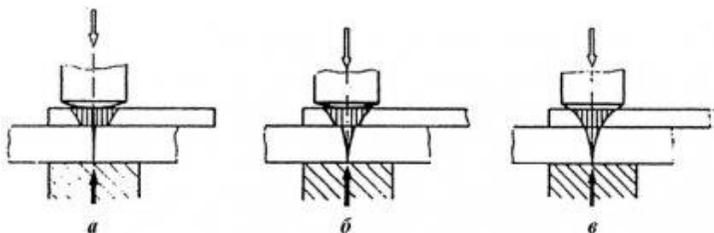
Распространение ультразвуковых колебаний при сваривании: а - начало сваривания; б - процесс сварки; в - окончание процесса [5].
